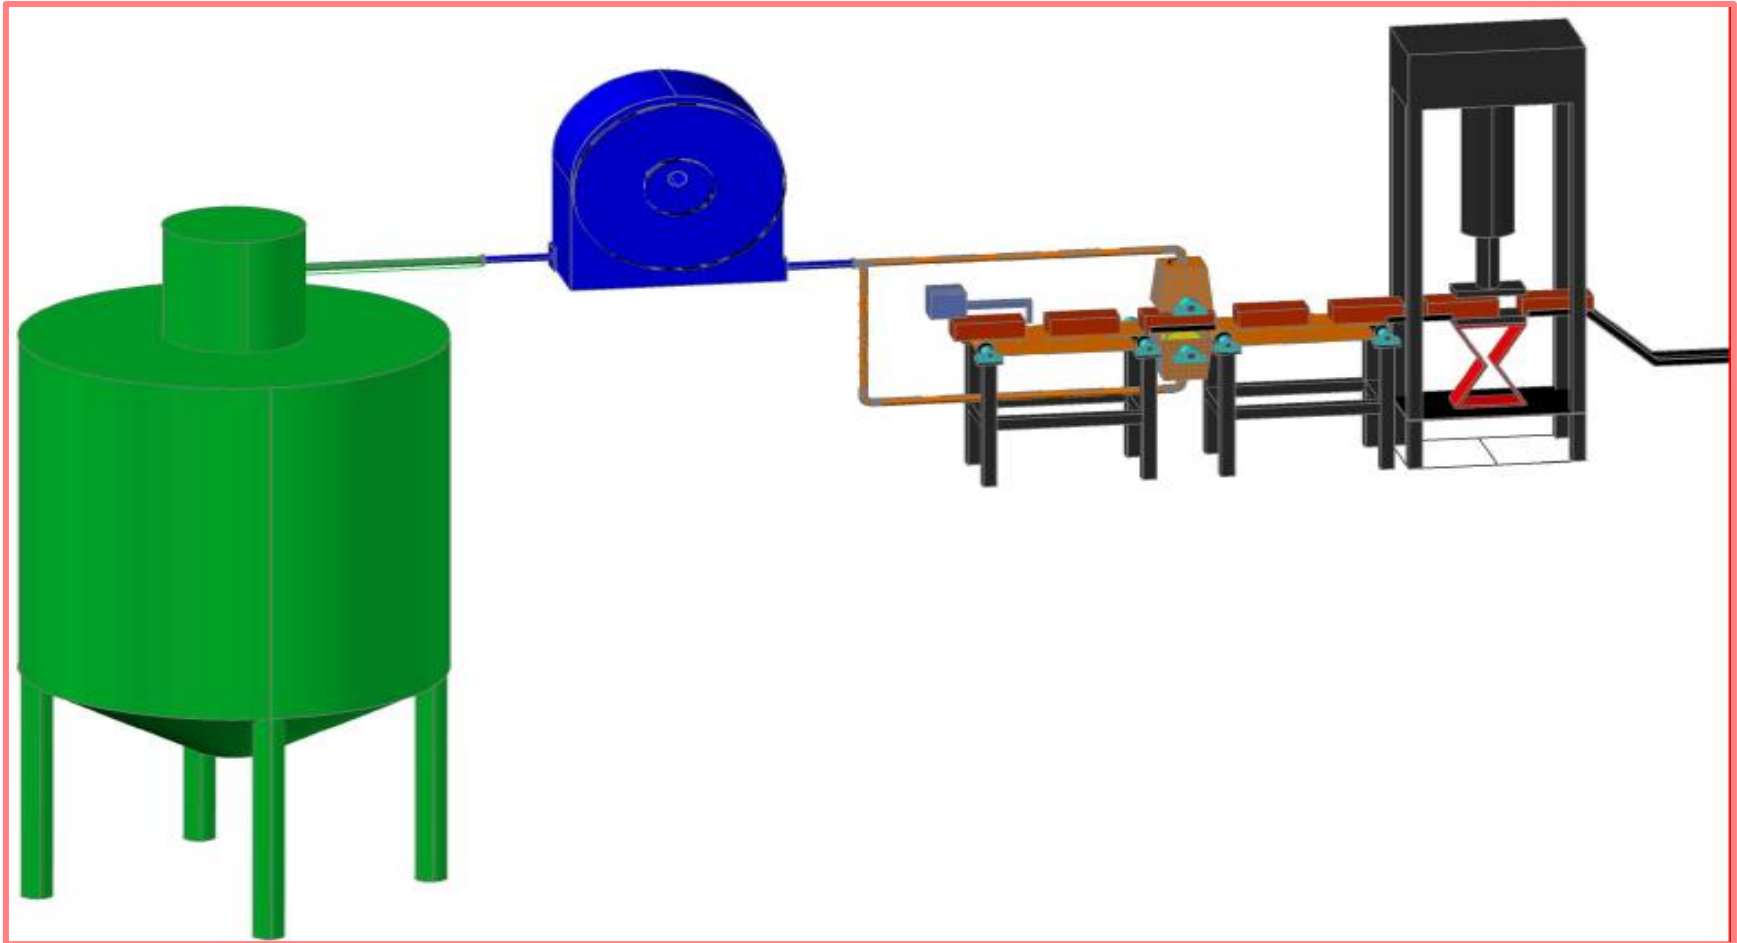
Vista isométrica de la máquina para producir espacatos. Fuente: Autor
